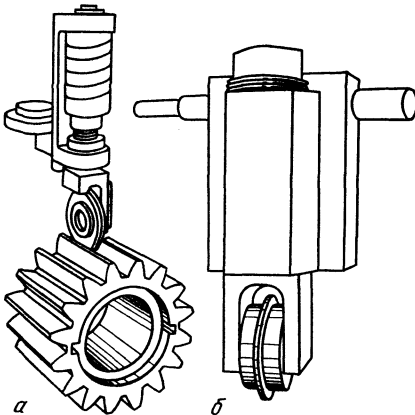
Роликовые державки для обкатки зубчатых колес:
